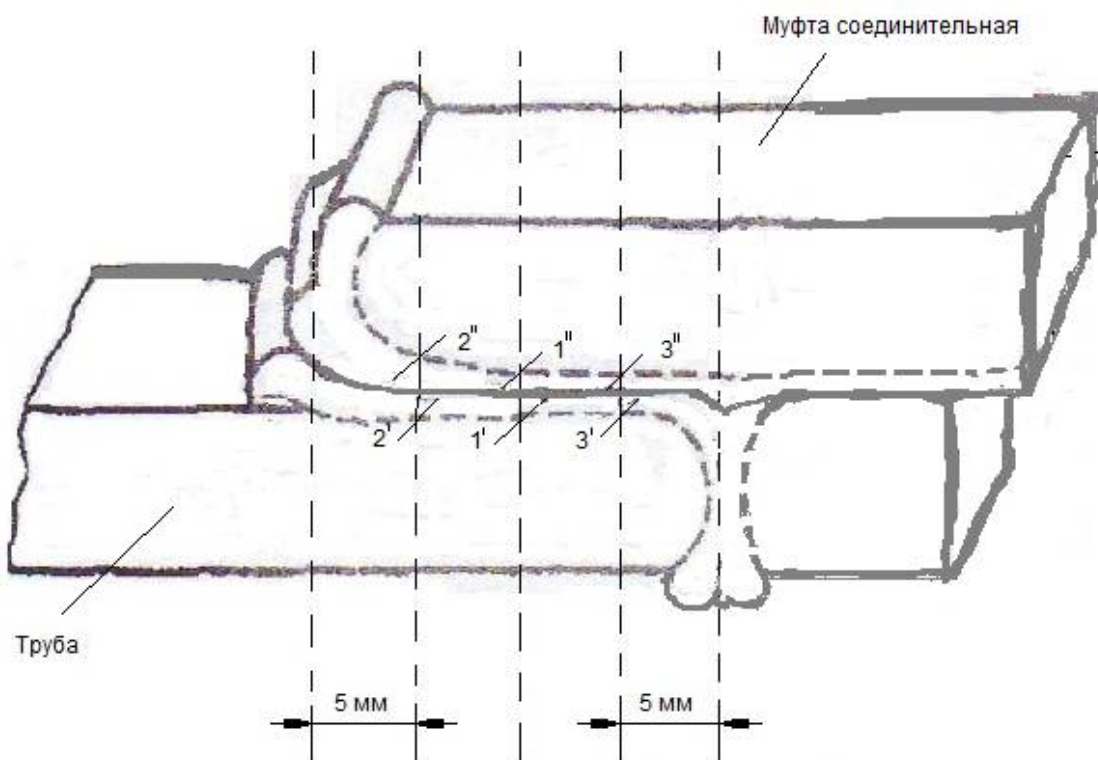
Схема участков измерения размеров области оплавления в раструбном сварном соединении
